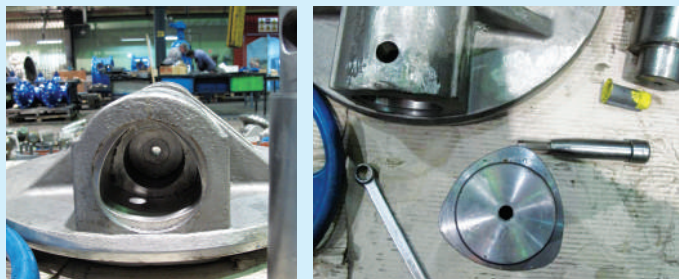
Крепление диска к валу с помощью призматической шпонки
